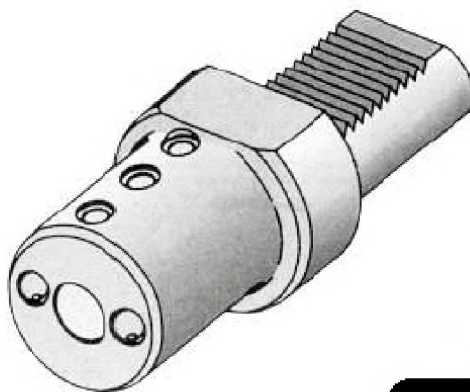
Осьовий різцетримач Е2-50х32 DIN1809
